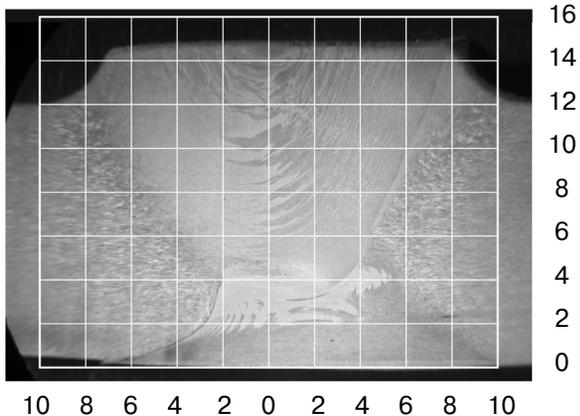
Макроструктура поперечного сечения сварного шва комбинации пластин АМг5 – 6082
